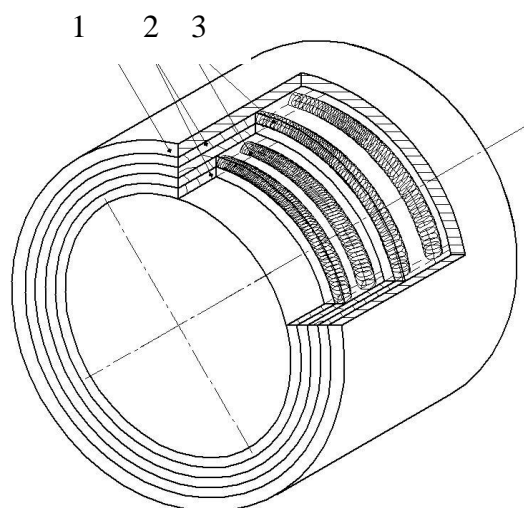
Схема вкладыша подшипника скольжения с металлическим пружинным наполнителем: 1 – опорная втулка; 2 – слой древесины; 3 – пружина
